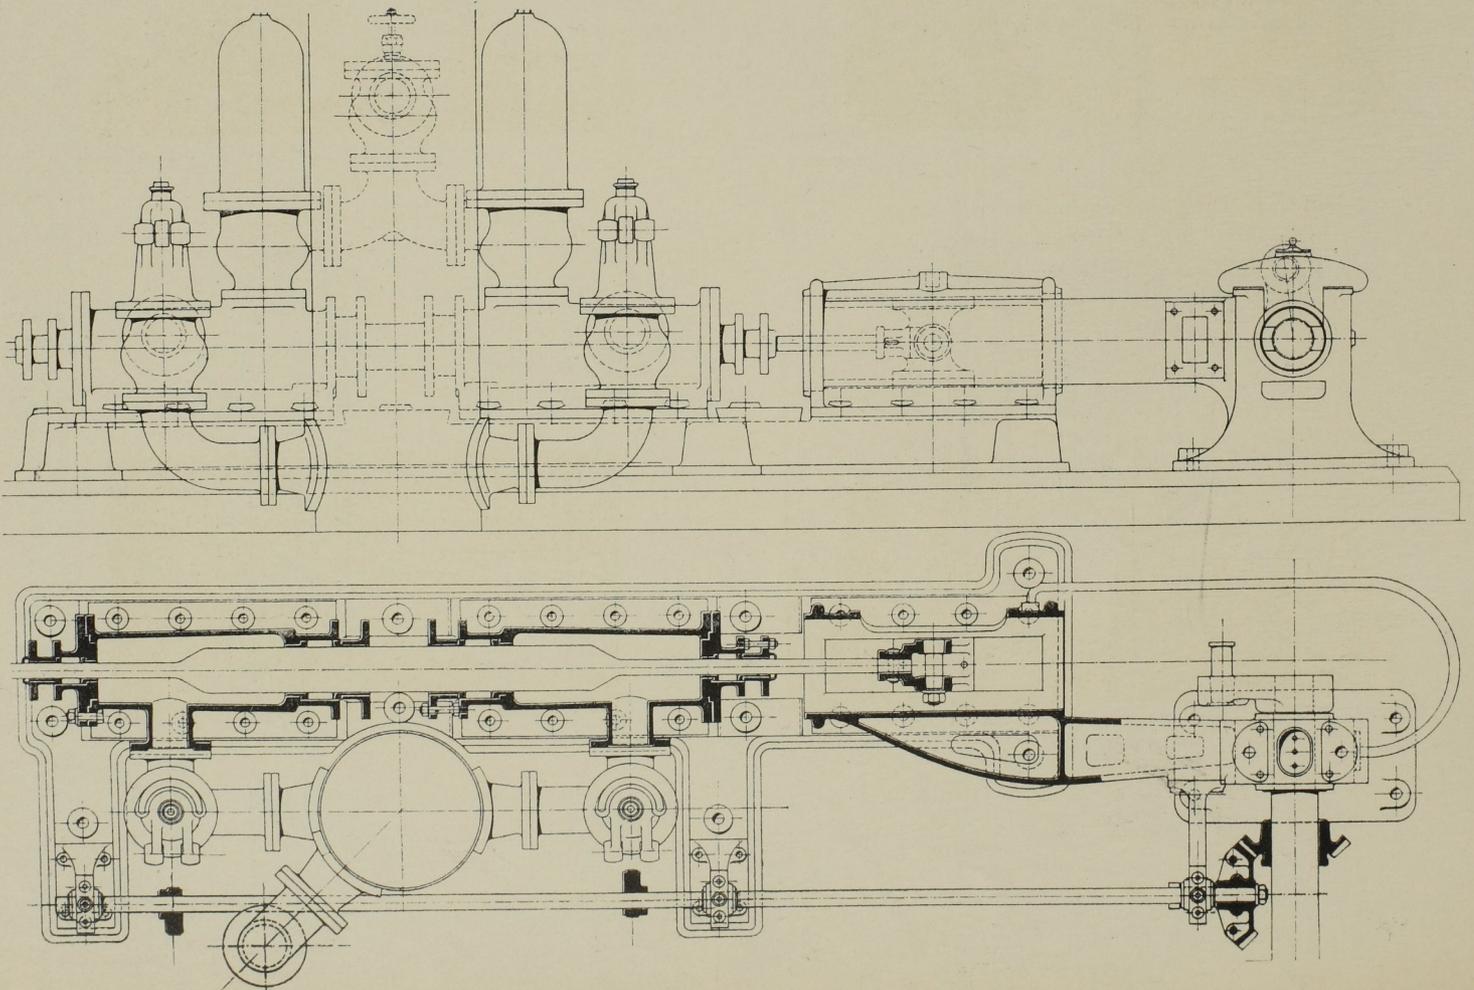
Seitenansicht und Grundriss der Pumpe für 1,2 cbm auf 110 m. Masst. 1:25.
